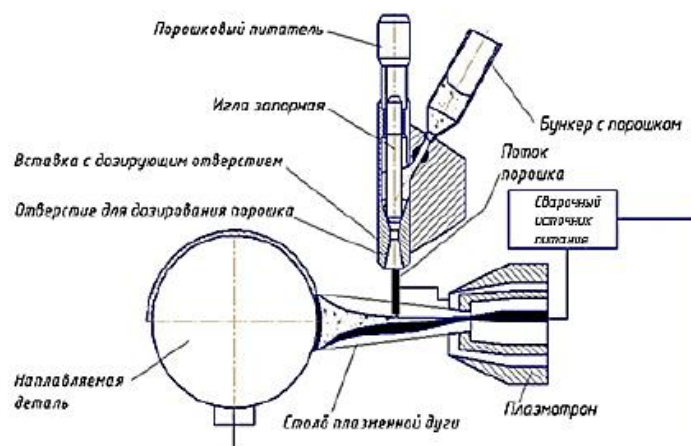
Схема плазменно-порошковой наплавки с внешним способом подачи порошка в дугу
